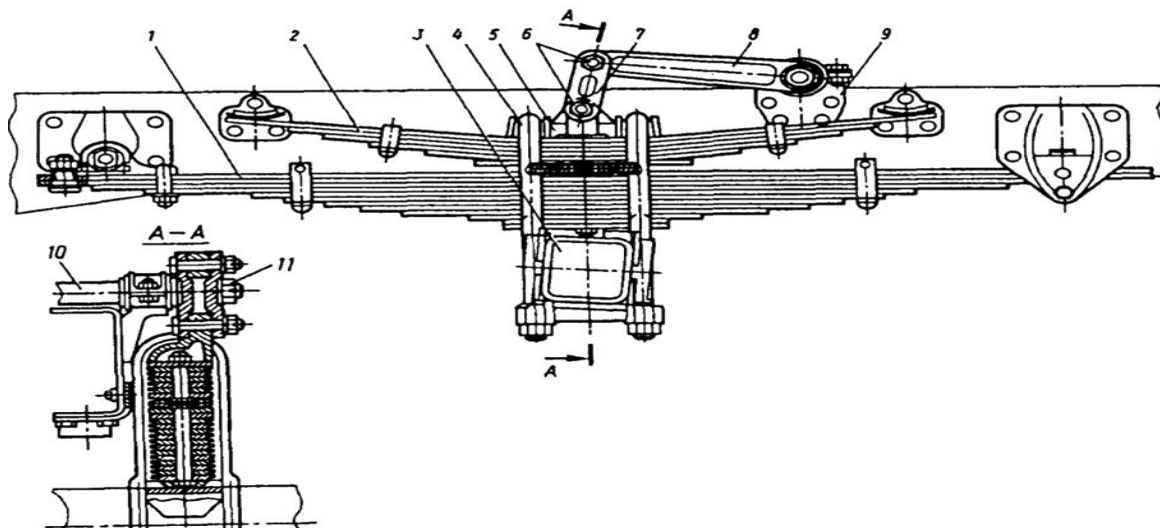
Рессорная передняя подвеска грузового автомобиля МАЗ
